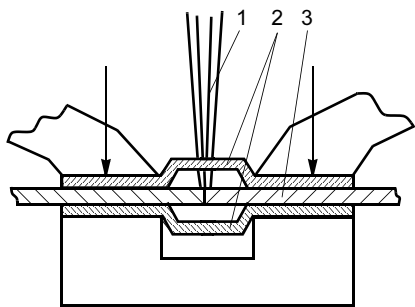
Схема сварки с использованием геттерной защиты
